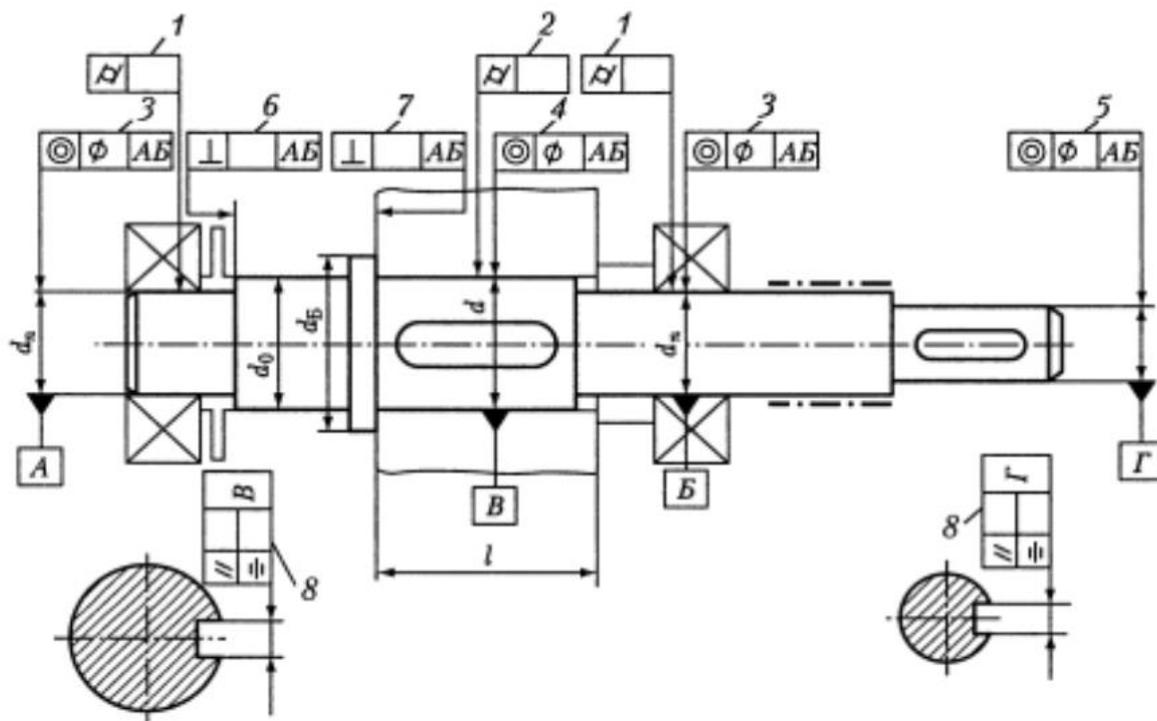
Допуски формы и расположения поверхностей вала
